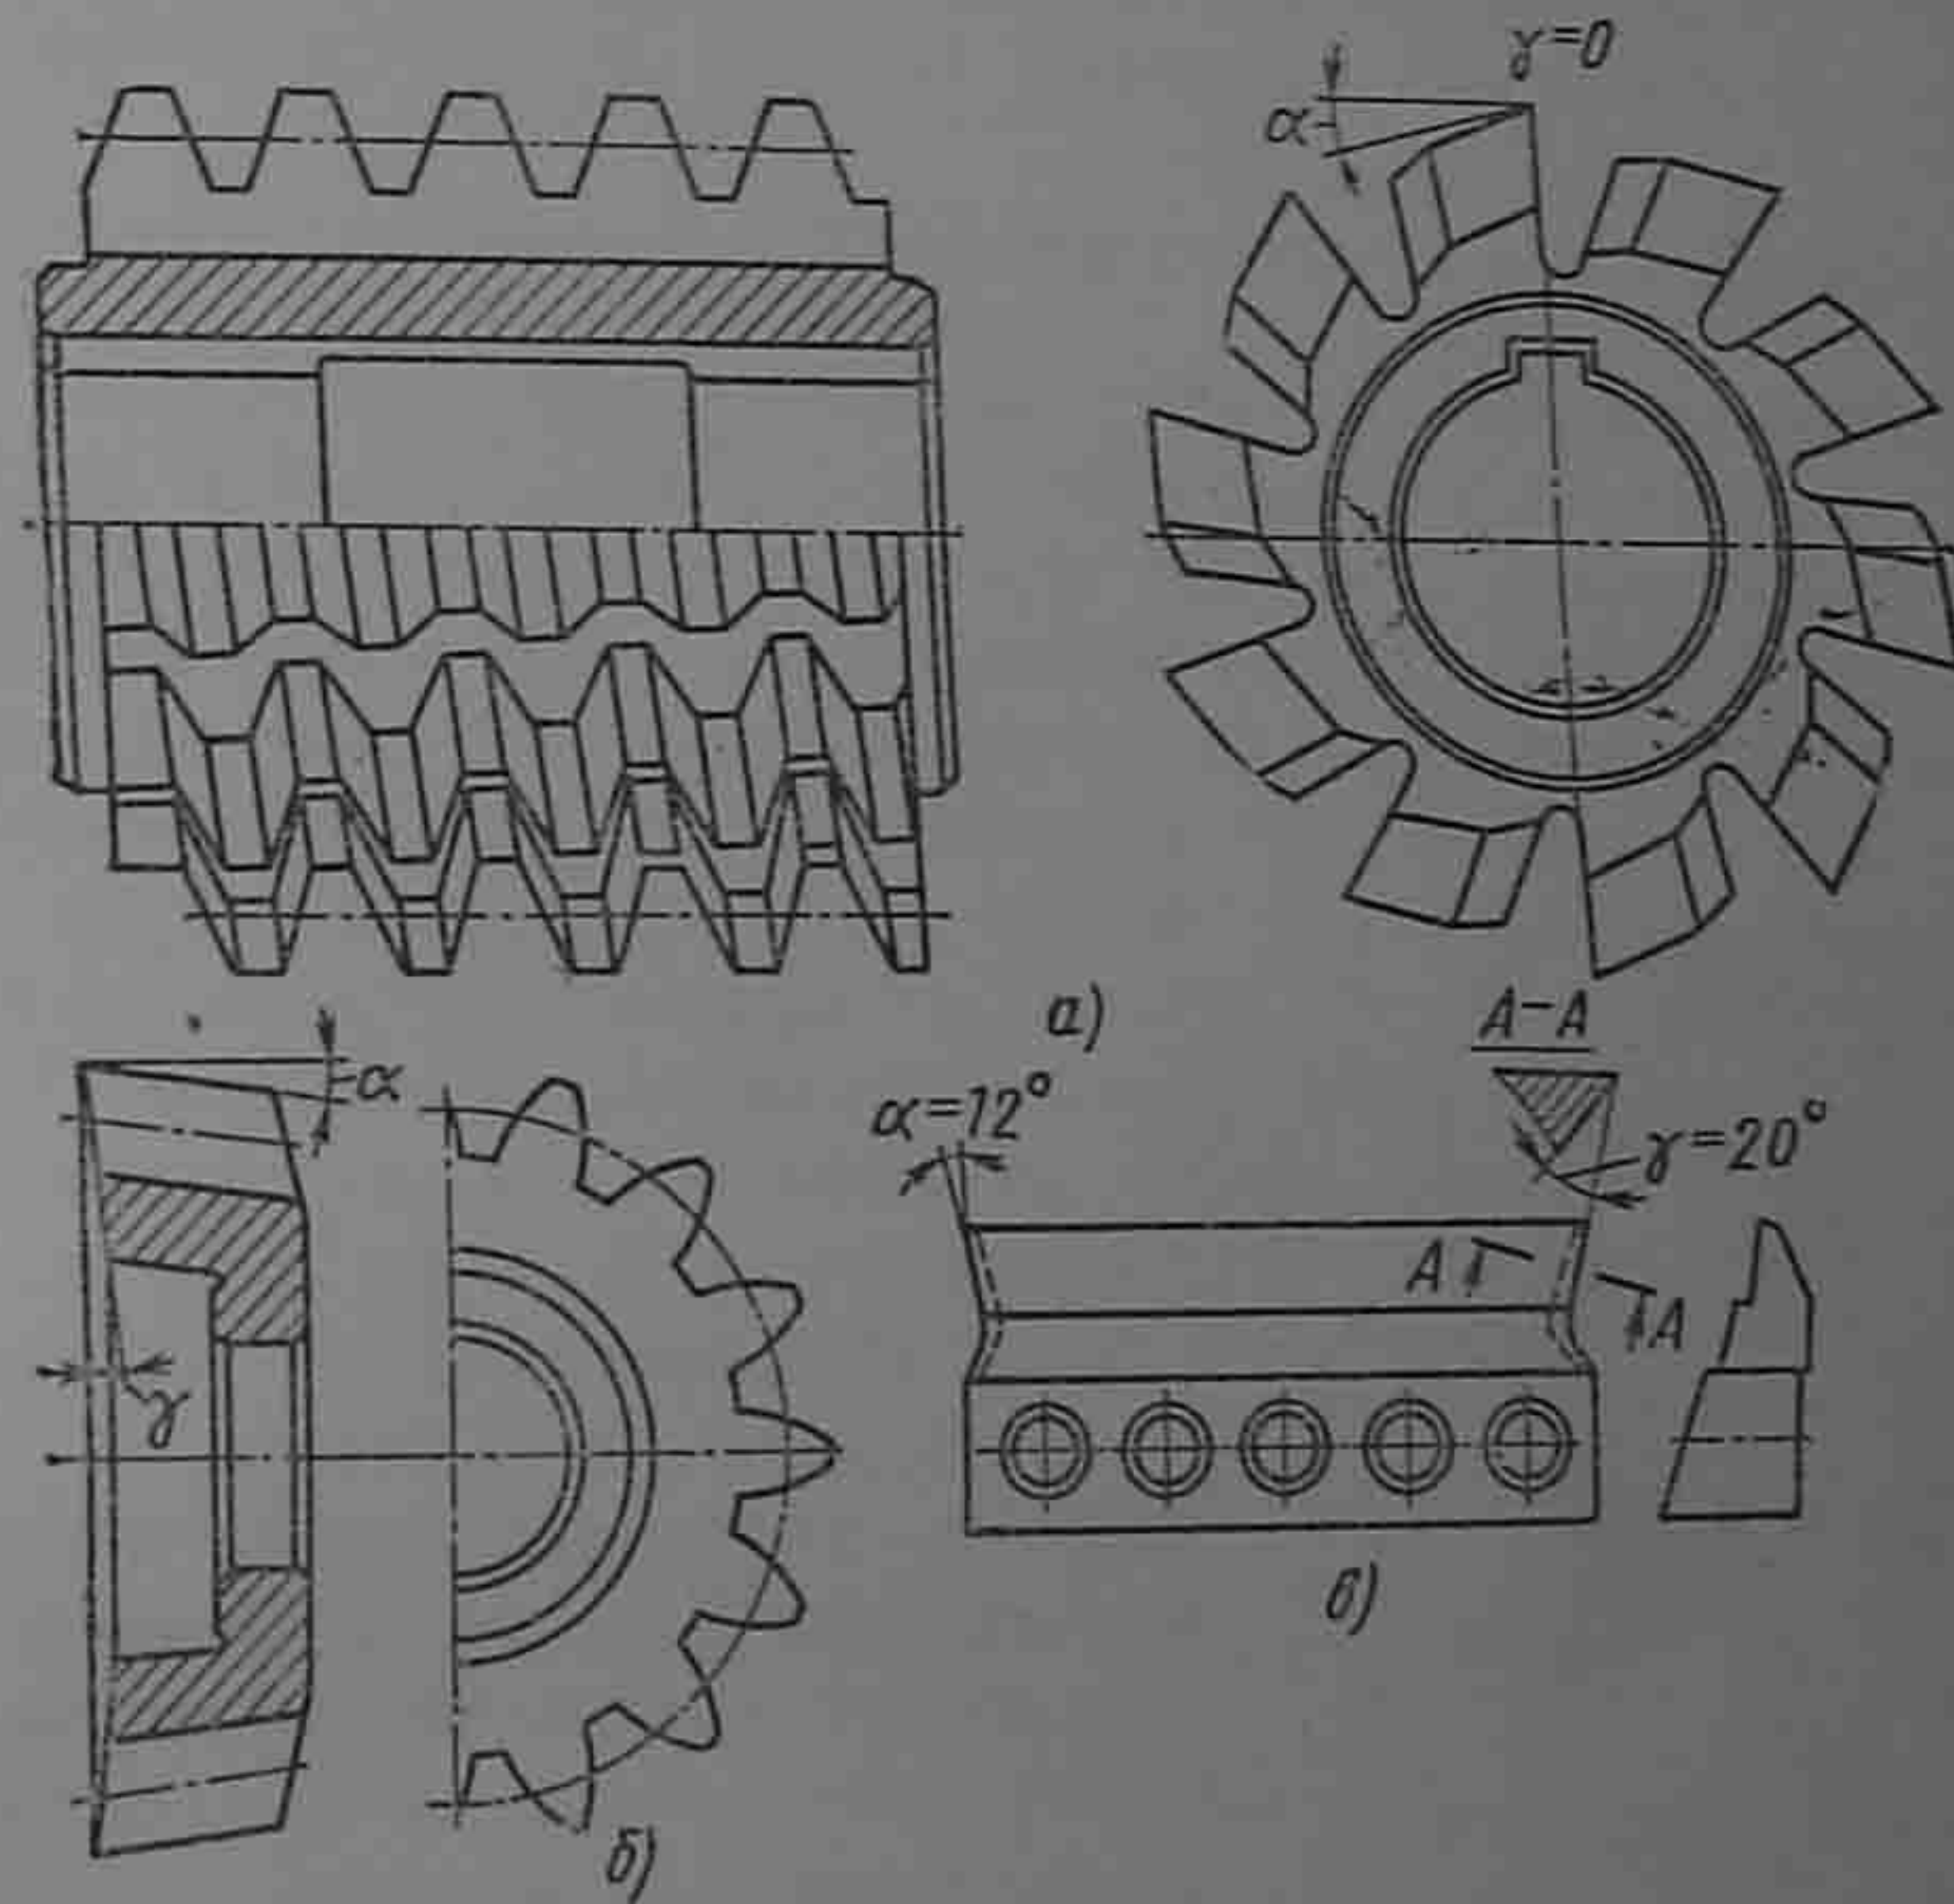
Червячная модульная фреза (а); зуборезный долбяк (б) и зубострогальный резец (а)
